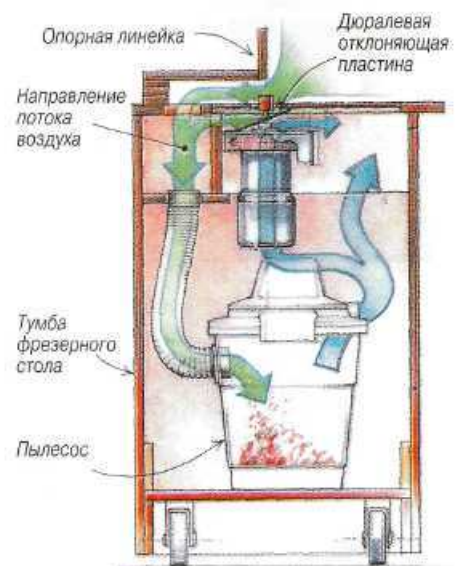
Схема воздушных потоков системы пылесбора фрезерного стола.
